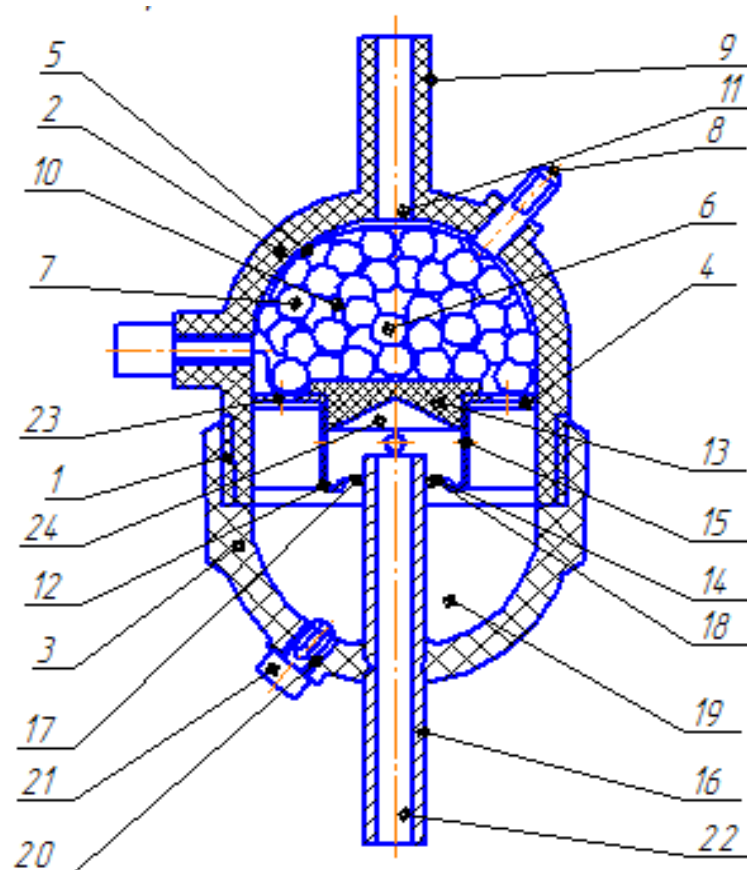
Устройство для электростатической обработки и очистки топлива
